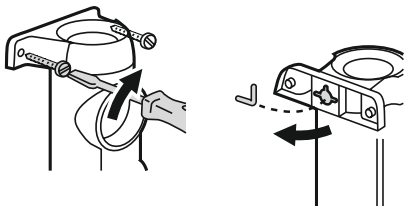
Крепление фильтра на поверхности / Figure 1 –Fastening the filter to surface /
